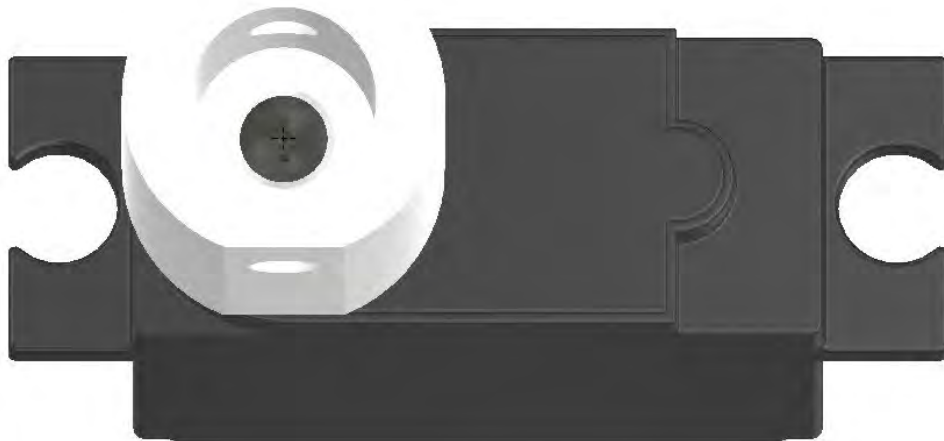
Servomotor atornillado a pieza de plástico para transmisión de torque. Fuente propia.
